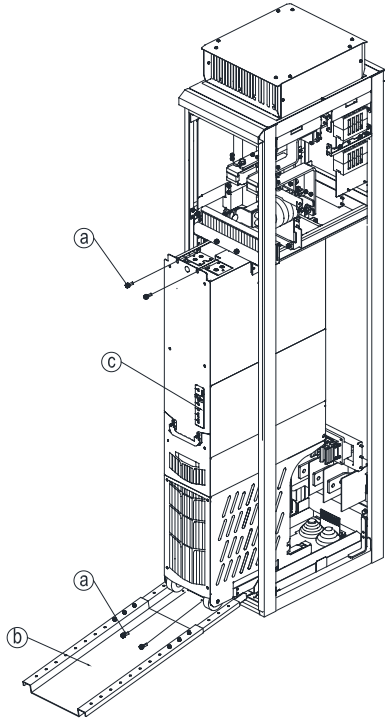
Замена вентилятора инверторного блока типоразмера Н8
